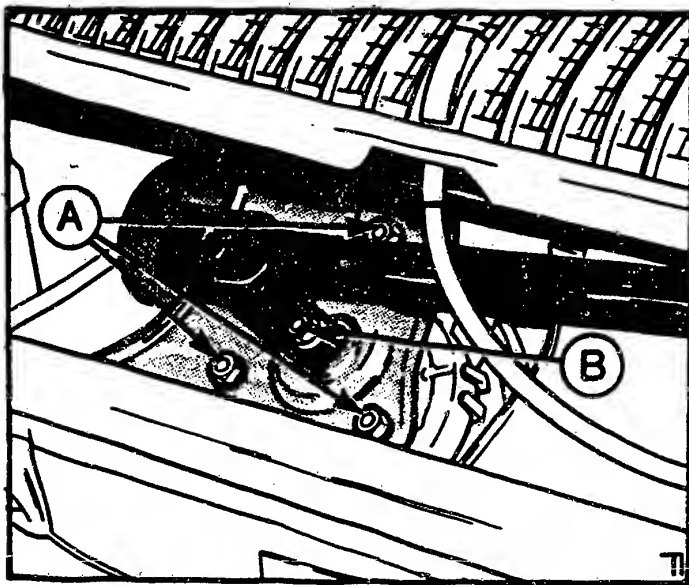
Zum Ausbau des Scheibenwischers ist dessen Motor so abzustellen, dass die Befestigungsschrauben A und die Mutter B gleichzeitig zugänglich sind.
